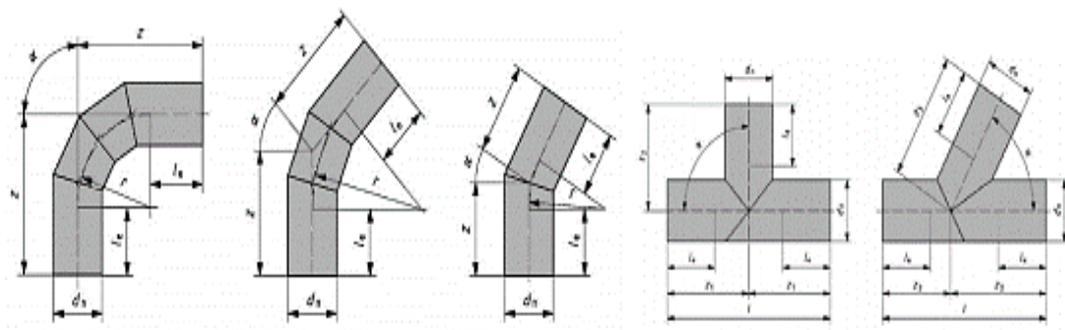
Accesorios manipulados de PE fabricados por soldadura a tope.
